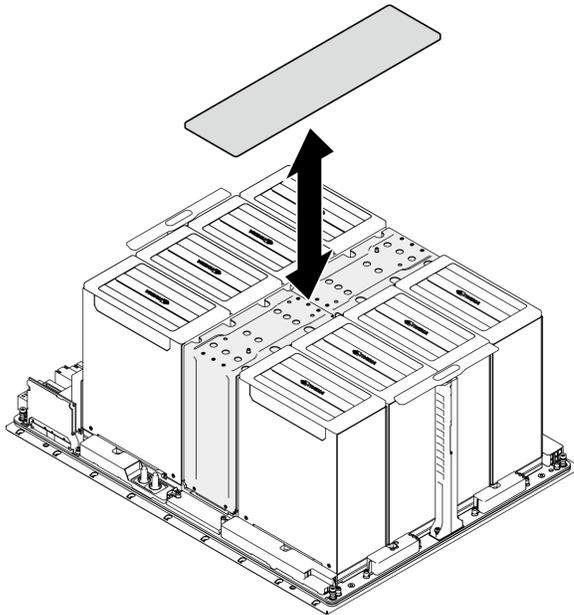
Remoção da tampa do dissipador de calor NVSwitch
